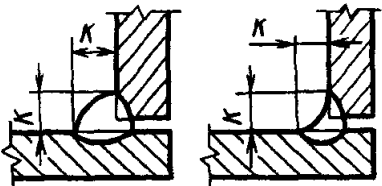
Положение корня шва в сварных соединениях
